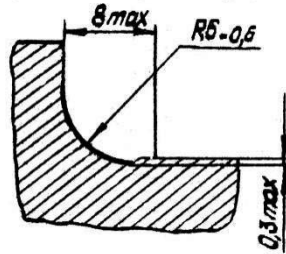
Схема обробки галтелі колінчастого валу після наплавлення шийки
